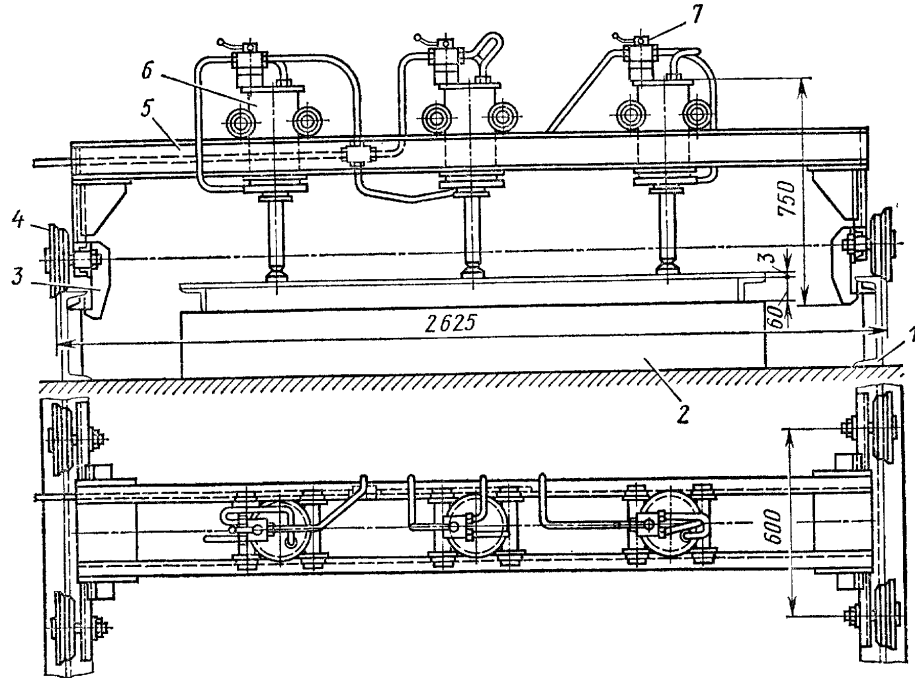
Катучая балка для сборки плосколистовых конструкций:
